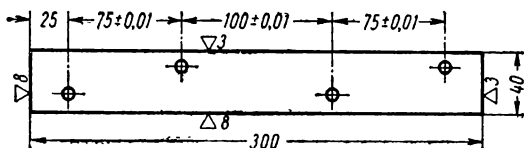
Деталь с длинной и короткой базовыми сторонами
